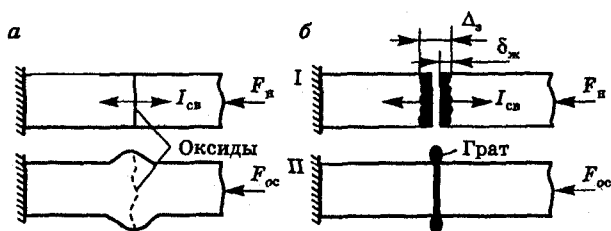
Этапы образования соединений при стыковой сварке: а — сопротивлением; б — оплавлением (Δ_z — зазор между деталями; $\delta_{ж}$ — слой расплавленного металла; F_n — начальное усилие; $F_{ос}$ — усилие осадки)
